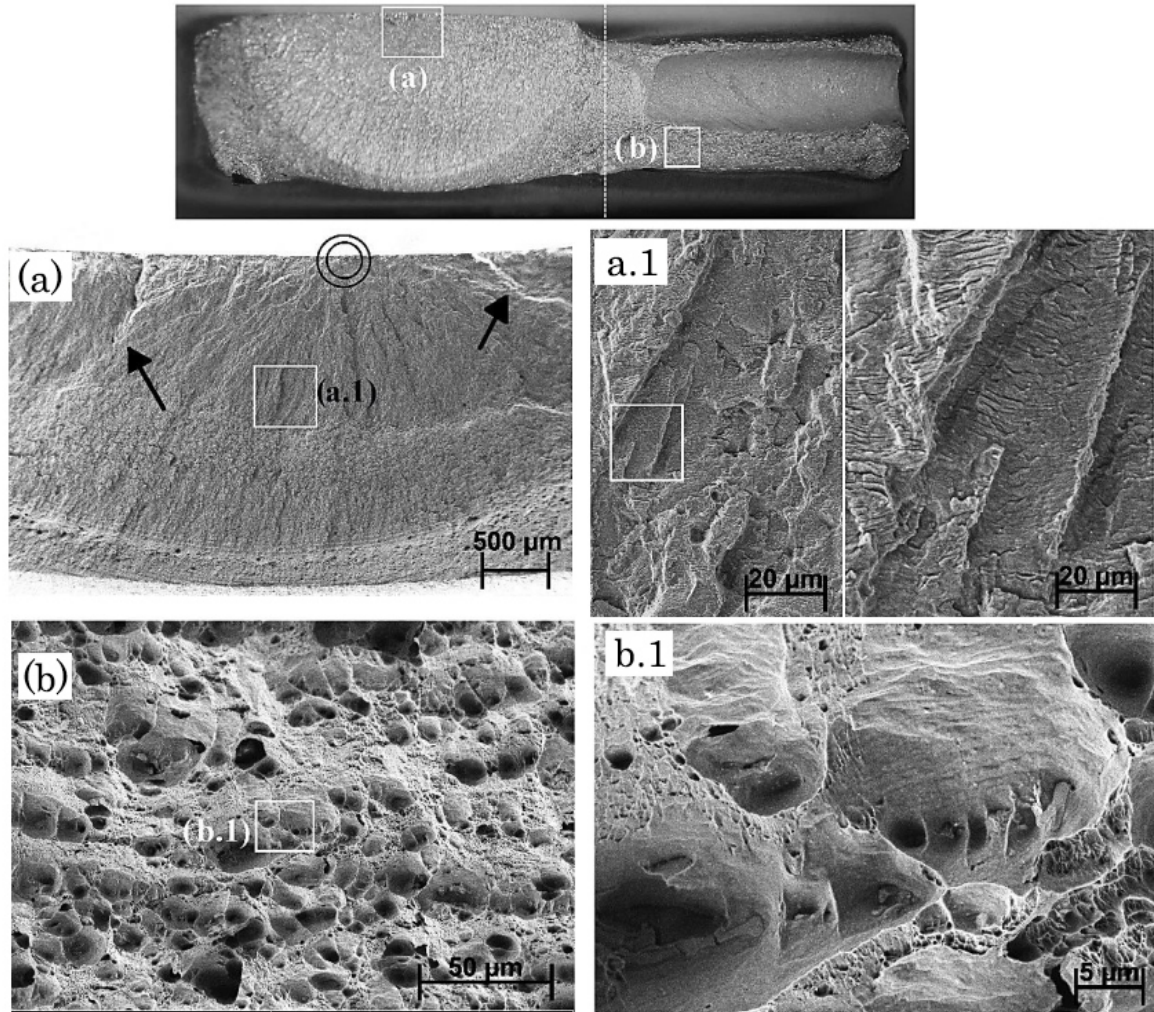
Superfície de fratura de amostra da soldadura DBPP-56-503_P6.
